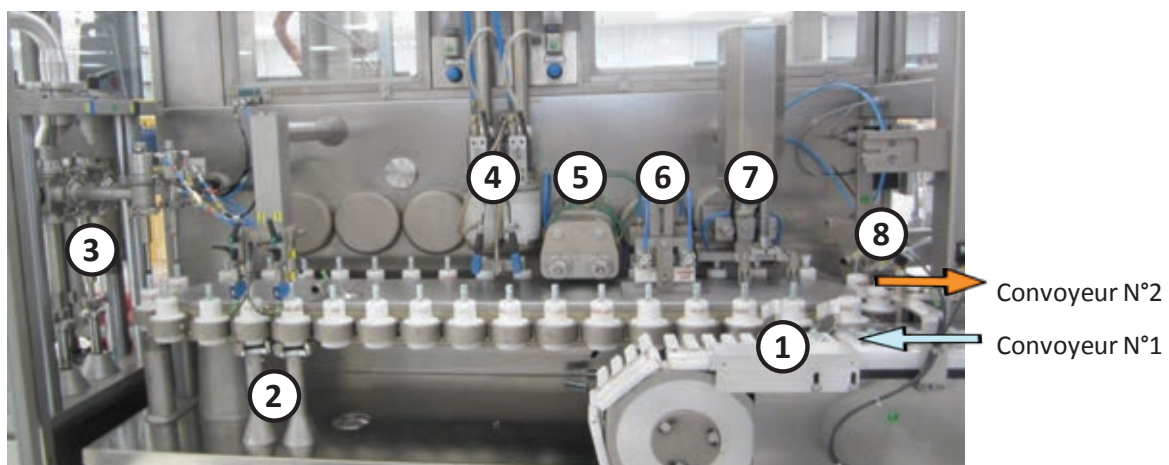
Organisation des postes sur le carrousel de la remplisseuse – Vue de face
